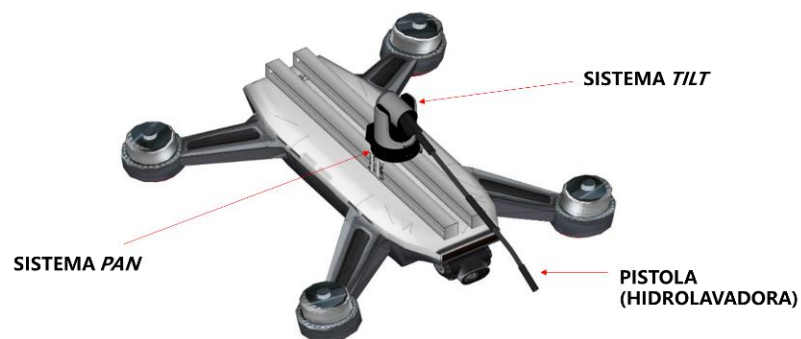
Dispositivo base, integrado con el sistema Pan-Tilt y efector final.
